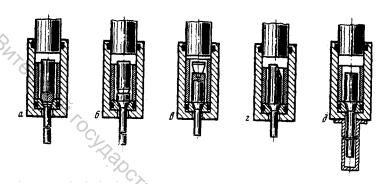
Способы торможения изделий при гидроэкструзии а — способ фиксации определённого остатка заготовки в матрице;
